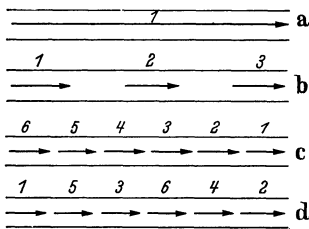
Schweißfolge bei Stumpf- und Kehlnähten.
